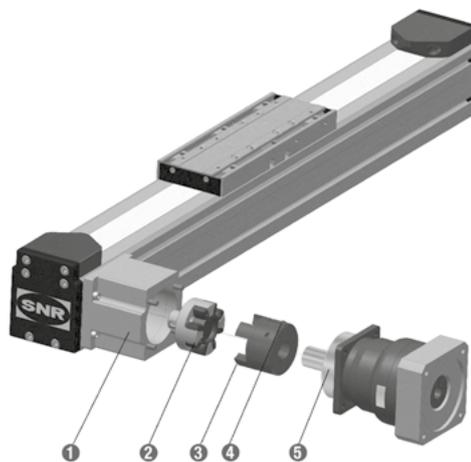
Motormontage an Linearachsen mit Zahnriemenantrieb und Kupplungsglocke
